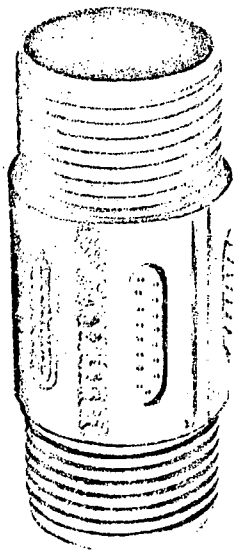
ESCARIADOR "STRIP TYPE"
